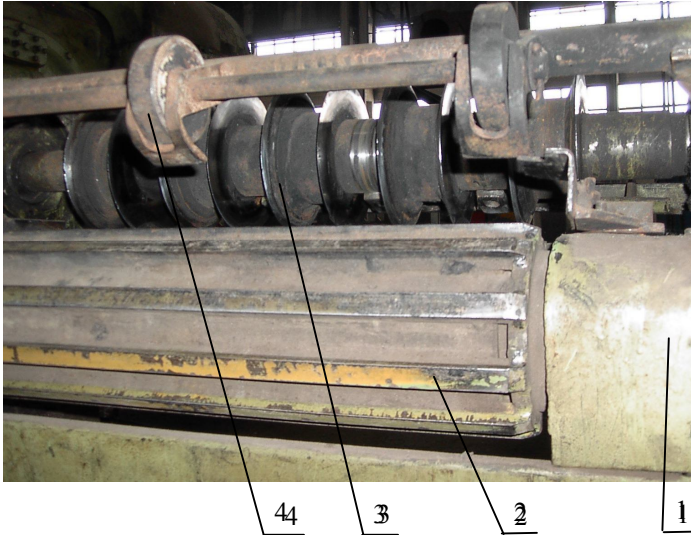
Конструкція високомодульної зубчато-шліцьової передачі для подачі конвеєрної стрічки в зону різання: 1 – привід; 2 – шліці; 3 – дискові ножі; 4 – притискний ролик конвеєрної стрічки
